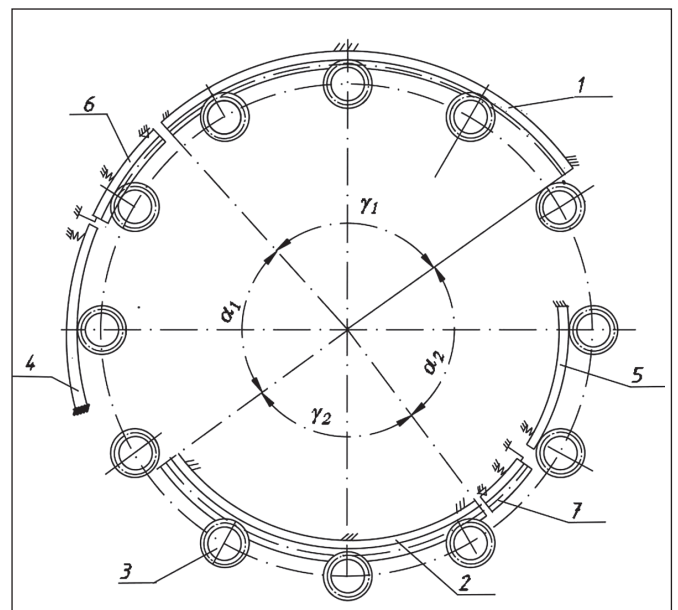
Схема бипланетарного механизма с размыканием кинематической цепи
